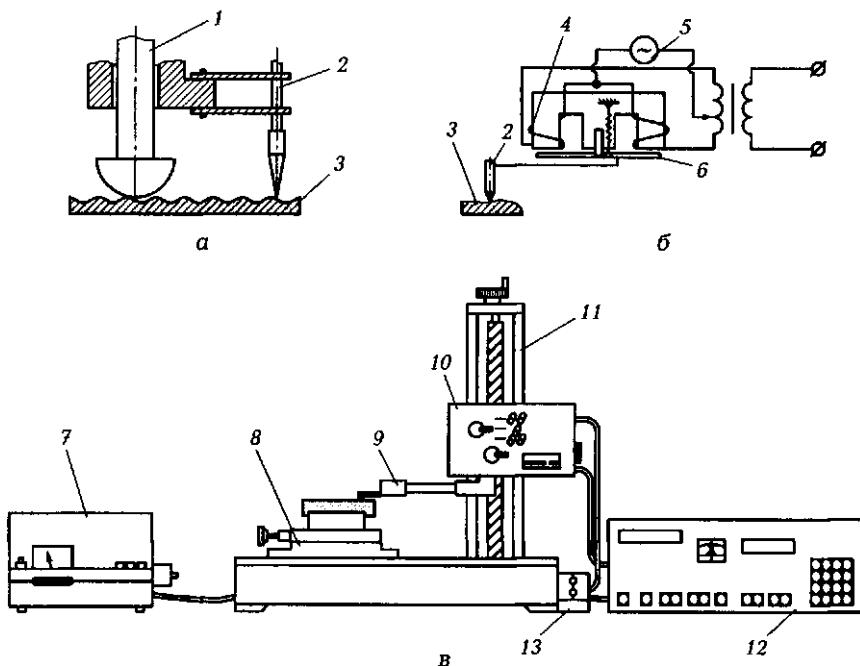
Контактный (щуповый) метод измерения шероховатости поверхности:
